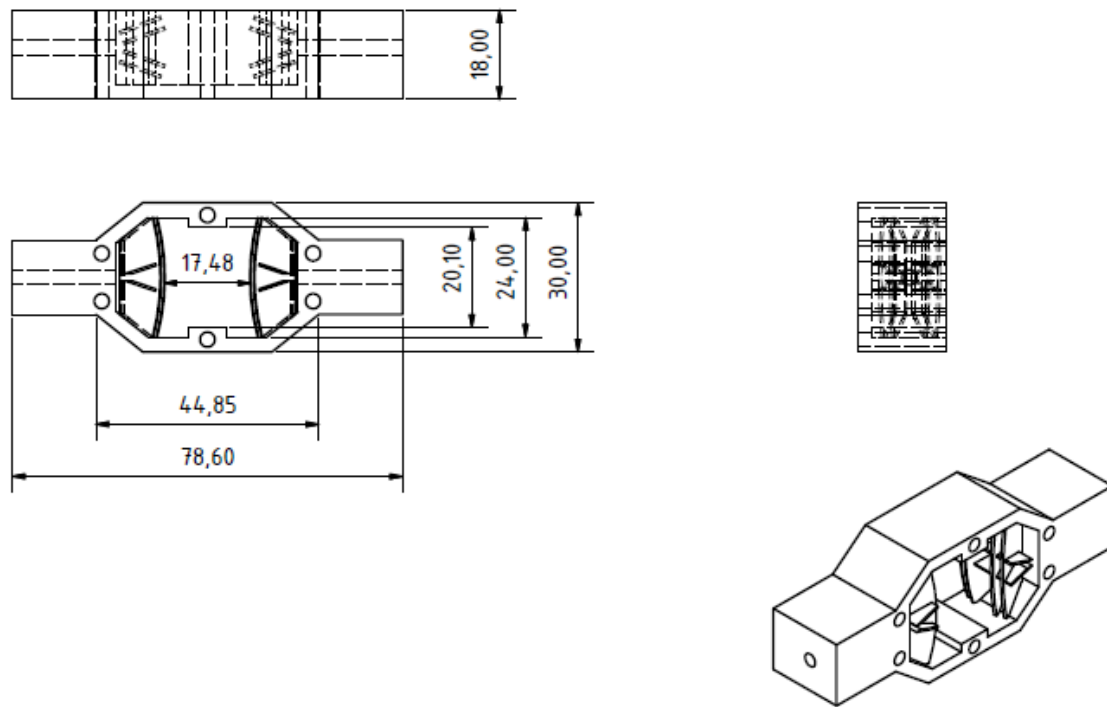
Technische Zeichnung des Enzymtransformationsmoduls in verschiedenen Ebenen inklusive Bemaßung.
